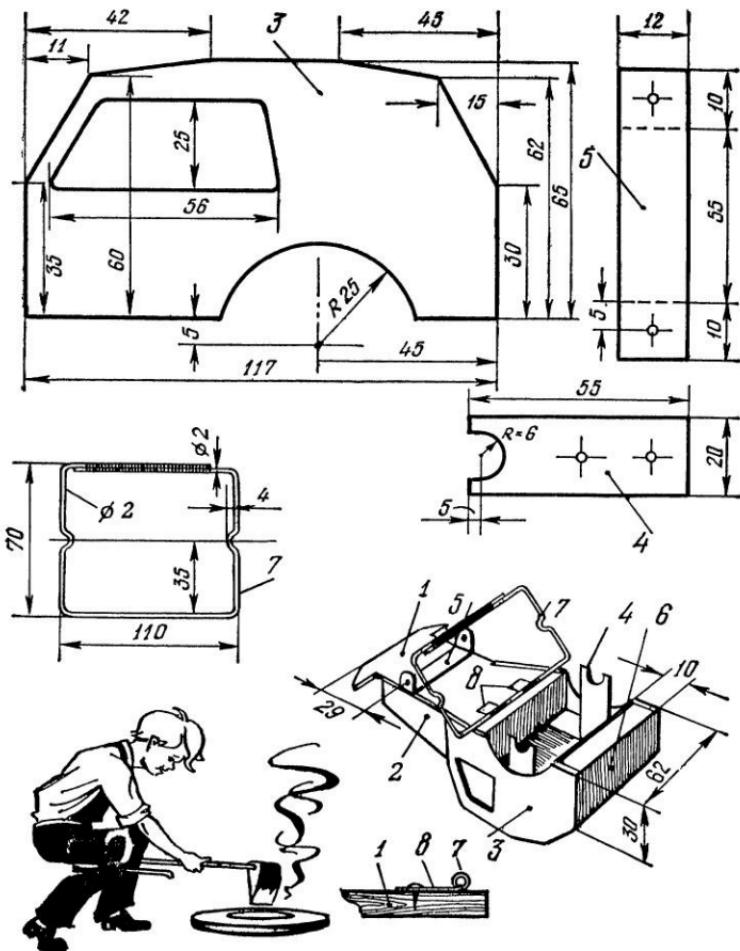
Боковые стенки вездехода и рамка резиномотора:
